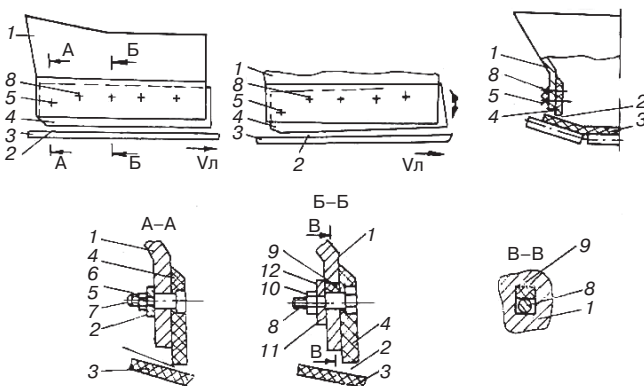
Схема борта ленточного конвейера [2]: 1 – ограждающий щиток; 2 – зазор; 3 – лента конвейера; 4 – уплотнительная полоса из ППФП-Астики; 5 – ступенчатый палец; 6 – гайка; 7 – шайба; 8 – ступенчатые болты; 9 – вертикальные пазы щитка; 10 – гайка; 11 – шайба; 12 – упругие элементы
